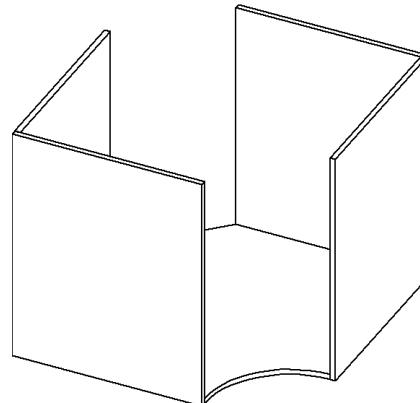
Частичная модель углового стола с установленными боковыми и задними стенками
